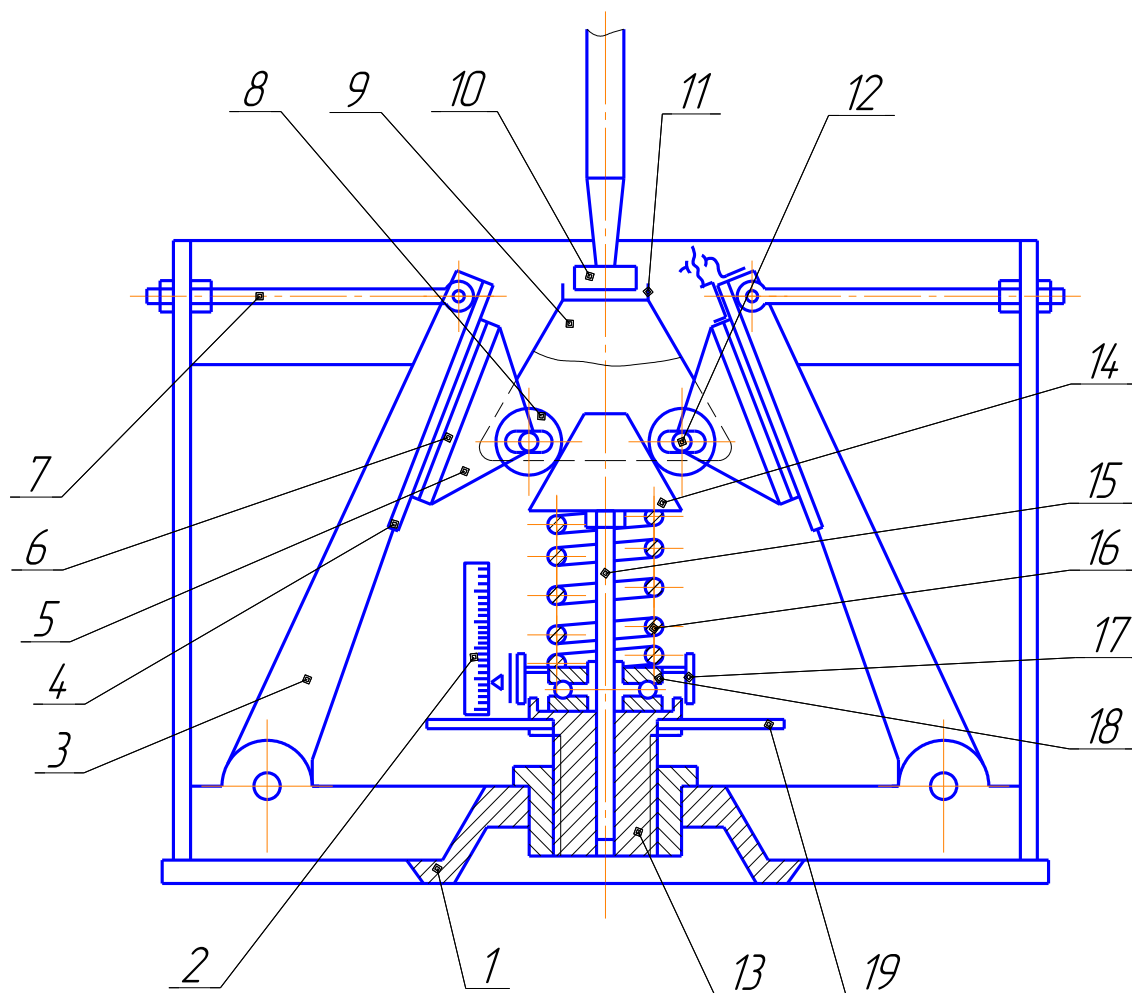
Принциповий устрій фрикційної виливниці
